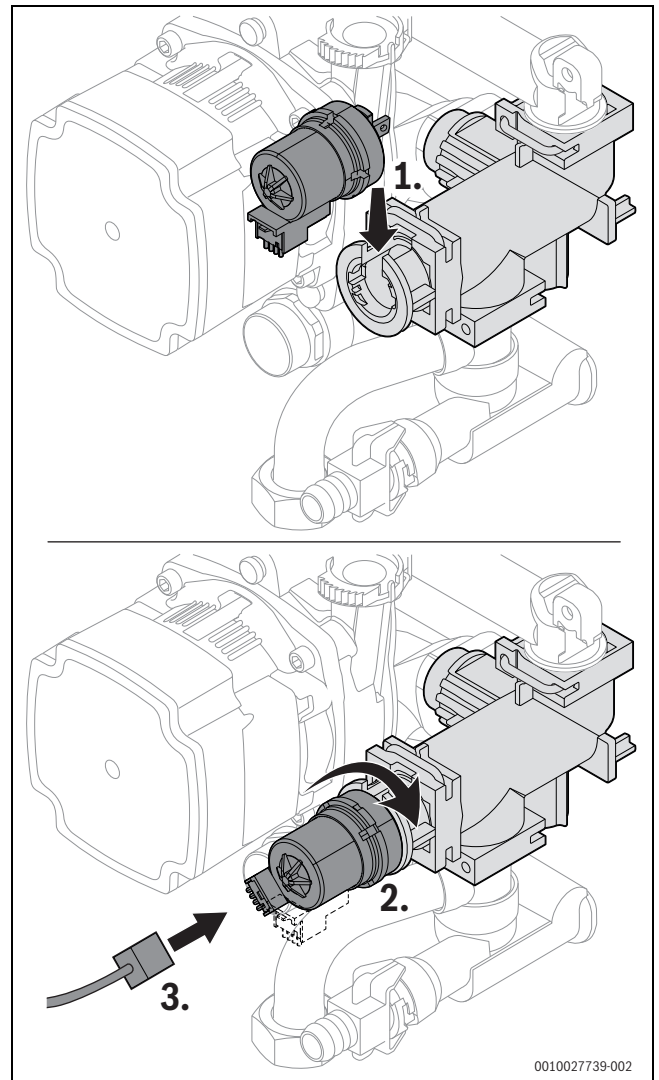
Montar el motor de la válvula de 3 vías (variante sin tornillos)
